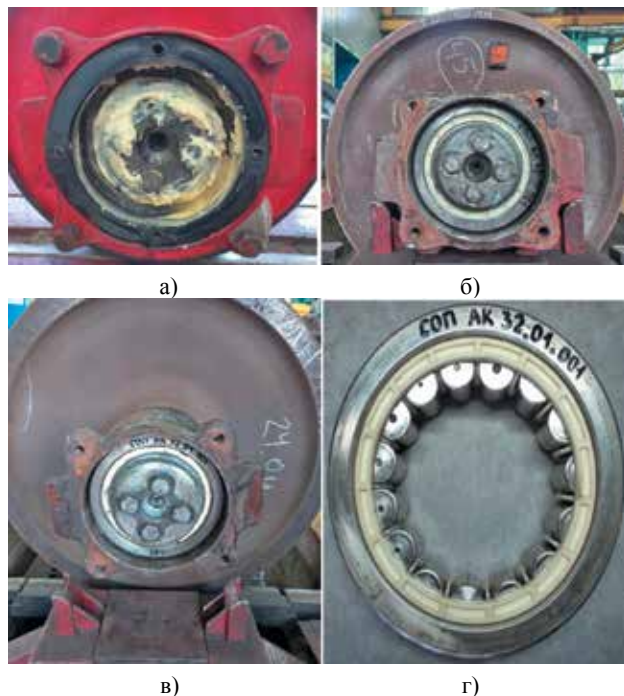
Общий вид сформированных колесных пар с СОП АК 32.01 в переднем подшипнике: а) толщина ободьев колес 25 мм (контрольный образец КО 18-07-08ВД); б) толщина ободьев колес 45 мм; в) толщина ободьев колес 65 мм; г) подшипник с дефектным роликом
